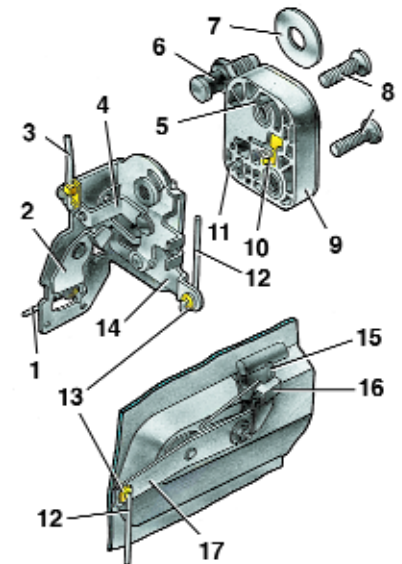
Внутренний и наружный замки двери: 1 – тяга внутреннего привода; 2 – рычаг внутреннего привода; 3 – тяга блокировки; 4 – рычаг блокировки; 5 – палец вилки запорного устройства; 6 – защелка замка; 7 – шайба защелки; 8 – винты крепления замков; 9 – корпус наружного замка; 10 – буфер защелки; 11 – палец собачки; 12 – тяга наружного привода замка; 13 – втулки; 14 – рычаг привода наружного замка; 15 – наружная ручка; 16 – рычаг наружной ручки; 17 – рычаг наружного привода
